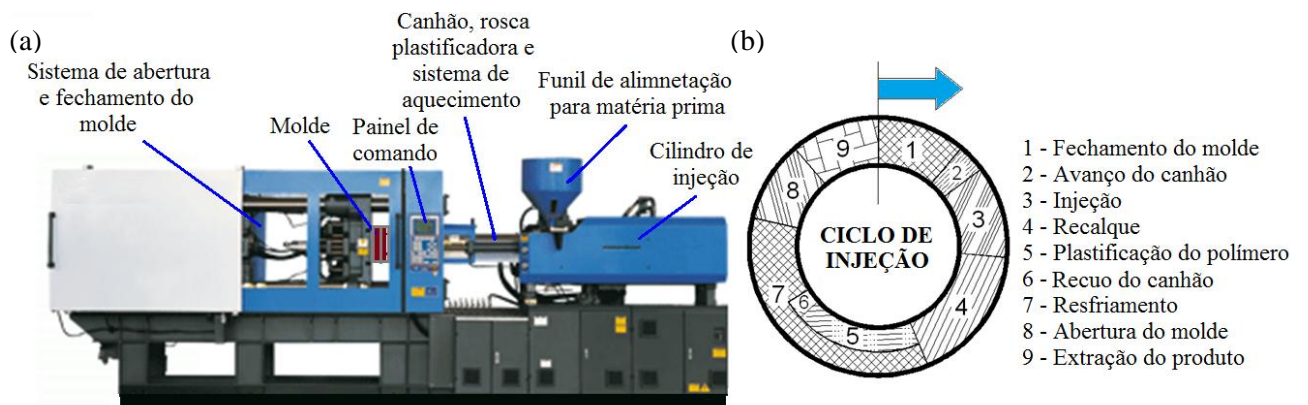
Equipamento e processo de injeção. (a) Máquina de moldagem. (b) Ciclo de injeção [40].
